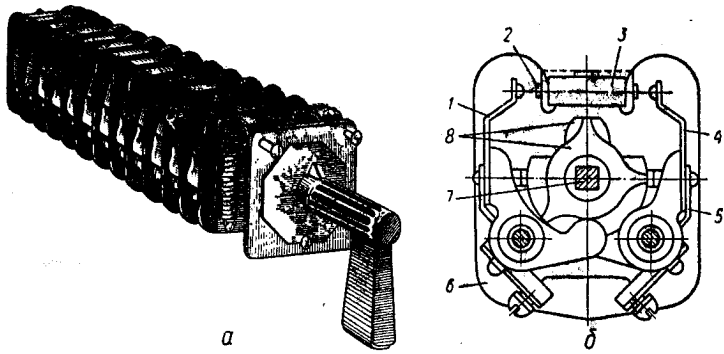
Общий вид (а) и секция (б) универсального переключателя: 1 — подвижный контакт; 2 — неподвижный контакт; 3 — изоляционная рейка; 4 — клемма; 5 — гибкое контактное соединение; 6 — изоляционная перегородка; 7 — валик; 8 — кулачковые шайбы
